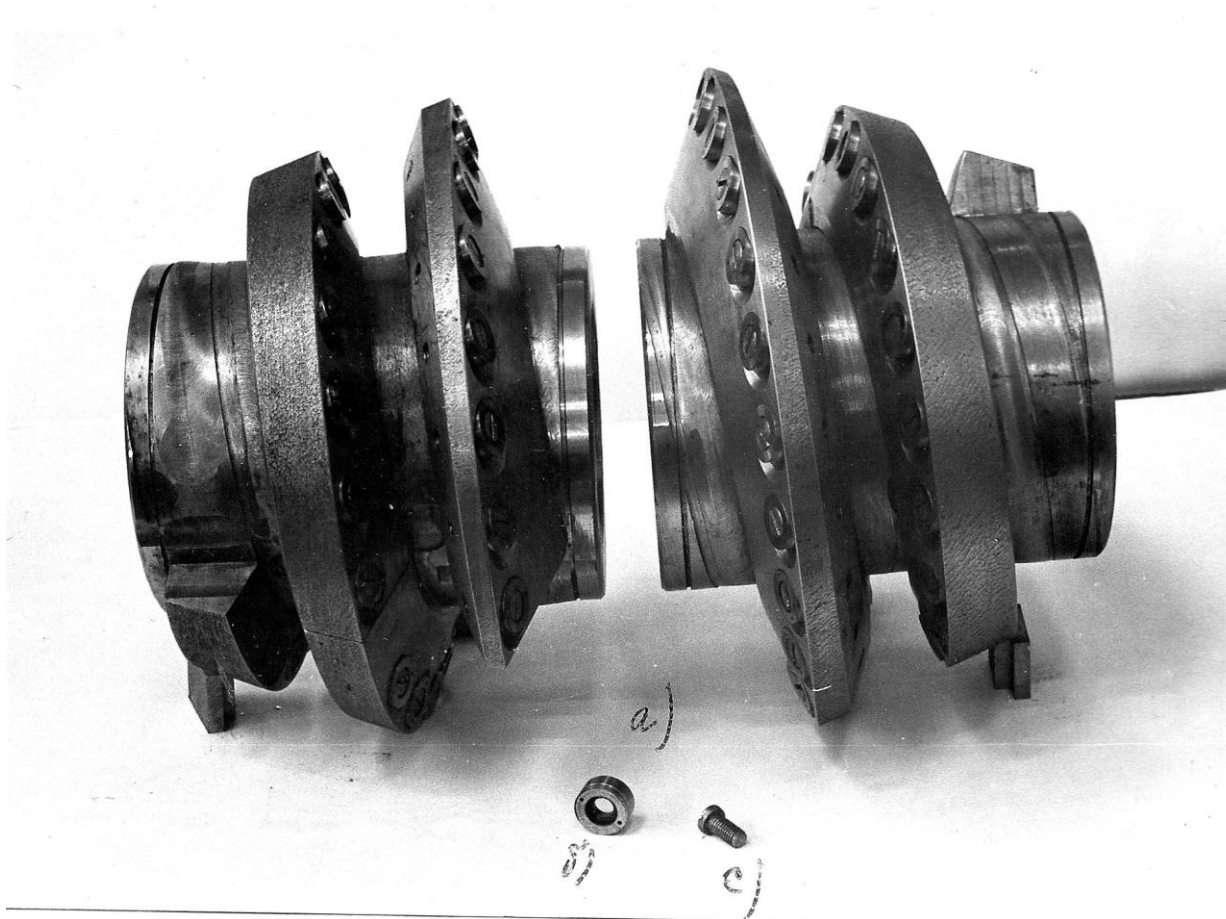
Специальная двухкорпусная фреза $m=28$ мм, оснащенная твердосплавными режущими роликами: а – левый и правый корпуса фрезы; б – твердосплавный ролик; с – крепежный винт
